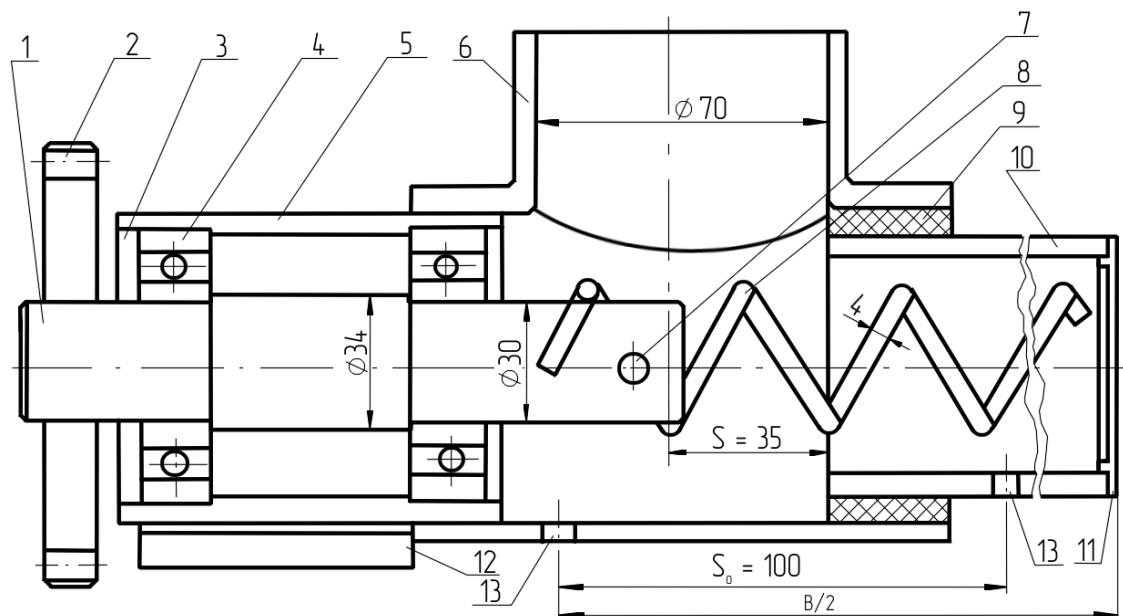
Вариант компоновки узла спирали с индивидуальным вращением: 1 – вал; 2 – звездочка; 3 – крышка; 4 – подшипник; 5 – корпус подшипников; 6 – тройник подачи жидкости; 7 – болт крепления рабочей спирали; 8 – спираль; 9 – сальник; 10 – кожух-штанга; 11 – заглушка; 12 – рама; 13 – высевное отверстие
